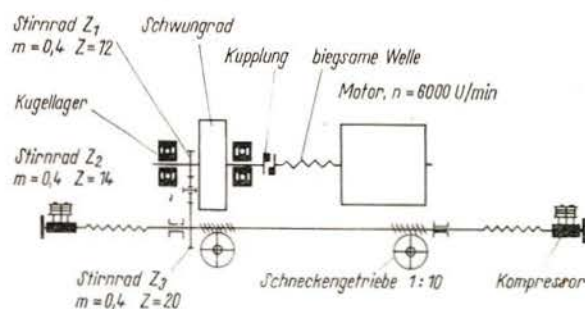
Das Getriebeschema zeigt den Kraftfluß vom Motor über die Schwungradwelle und Stirnräder auf die Schneckengetriebe der Radsätze.
